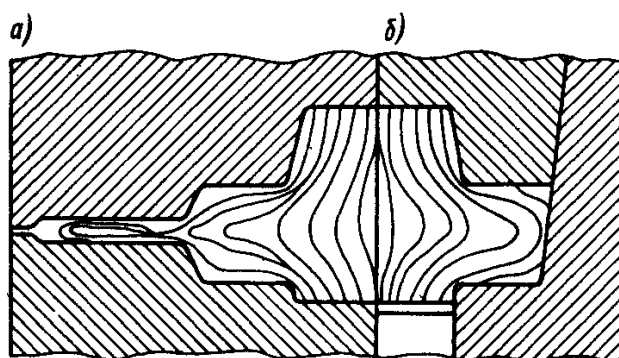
Схема расположения волокон металла при открытой (а) и закрытой (б) штамповке
